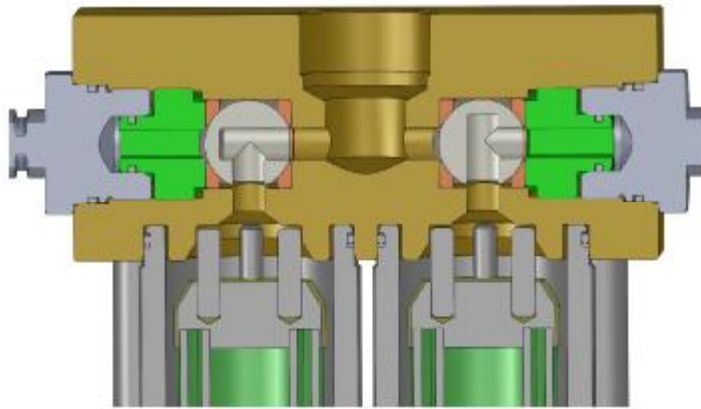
Demontaż przyłącza przepłukiwania zwrotnego
